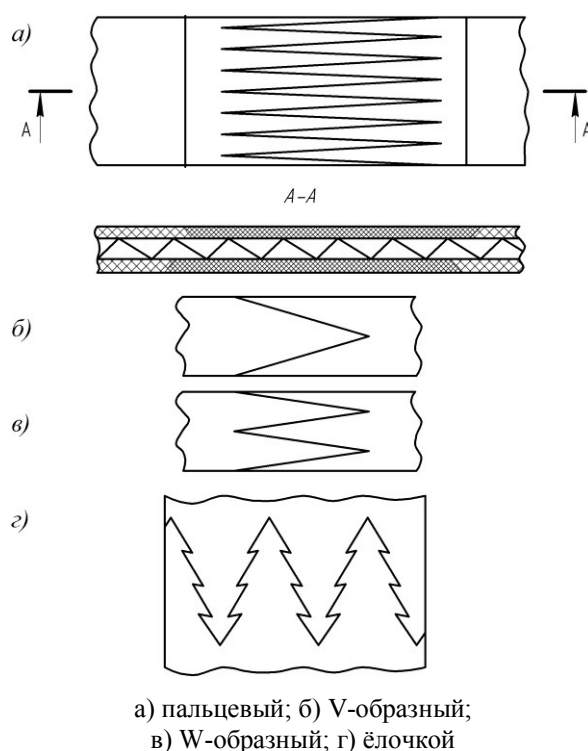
Конструкции бесступенчатых профильных стыков конвейерных лент
